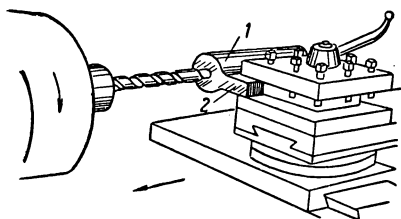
Установка сверл в державке, закрепляемой в резцедержателе.
